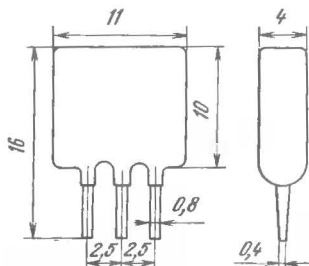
Габаритные и присоединительные размеры фильтров ФП1П8-62 и ФП1Р8-63
